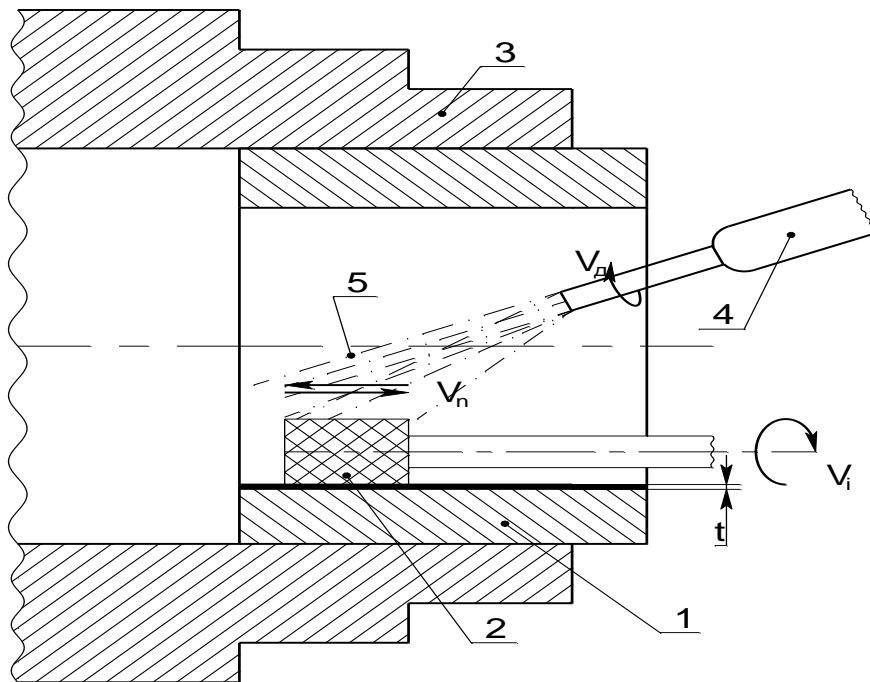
Спосіб фінішної прецизійної оздоблювальної обробки отворів деталей обертання з високолегованих композитів
